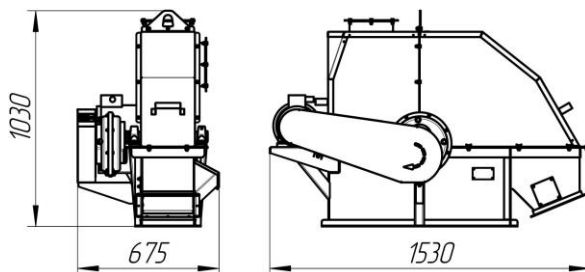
Станция приводная нории Н-25. Размеры габаритные
